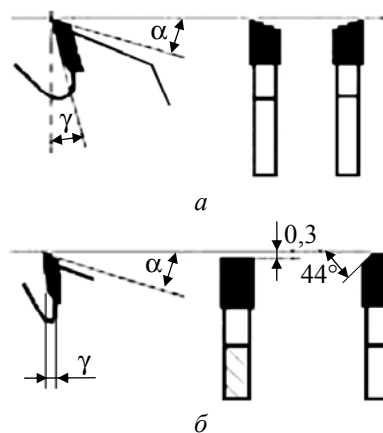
Профили зубьев дисковых пил с пластинами твердого сплава для распиловки ламинированных ДСТП:
